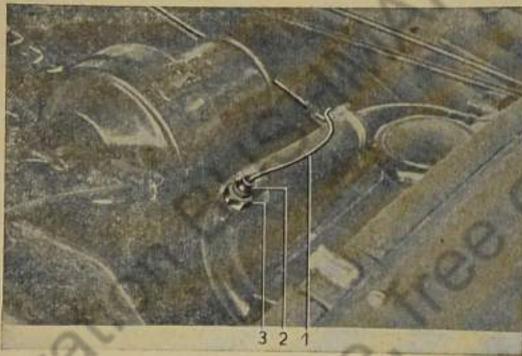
Fühler für Kühlwasser-Fernthermometer abschrauben
